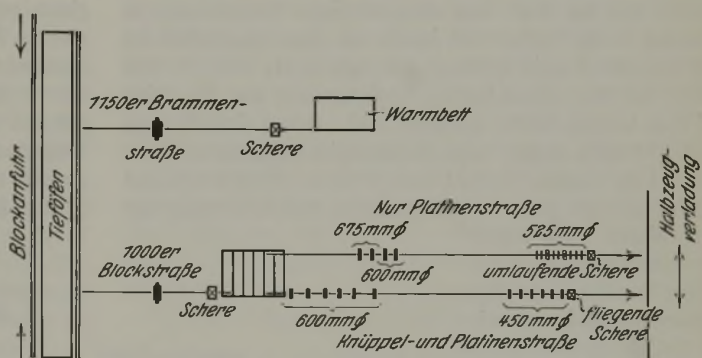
Anlage der Block- und Halbzeugstraßen der Bethlehem Steel Co., Sparrows Point.
